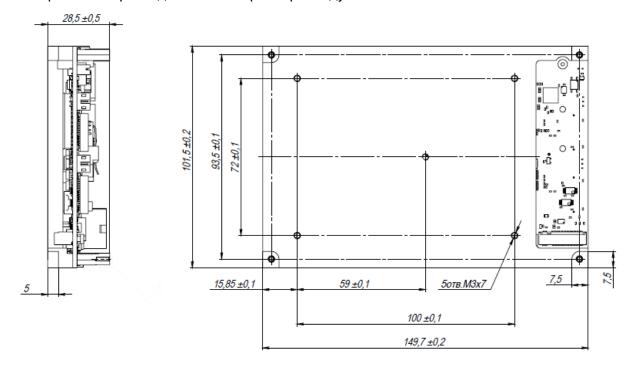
1 – Габаритные и присоединительные размеры модуля
